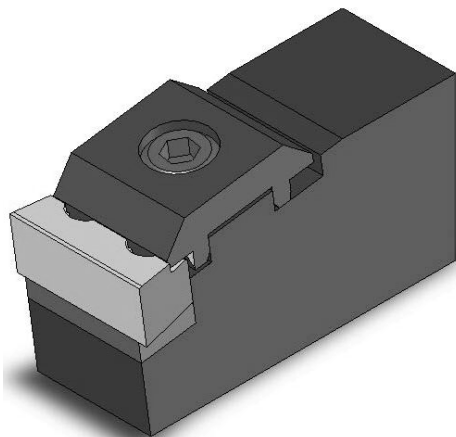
Сборный прорезной резец для тяжелых станков
